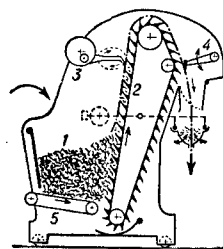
Разрыхлительная машина с игольчатой решёткой (самовес): 1 — камера; 2 — транспортёр; 3 — разрыхляющий орган; 4 — съёмный валик; 5 — подающая решётка.
